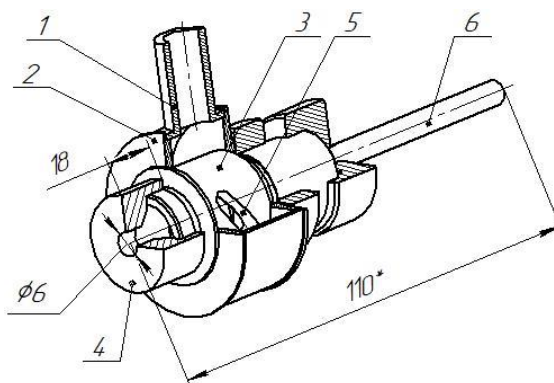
Форсунка з двома нахиленими підвідними каналами
